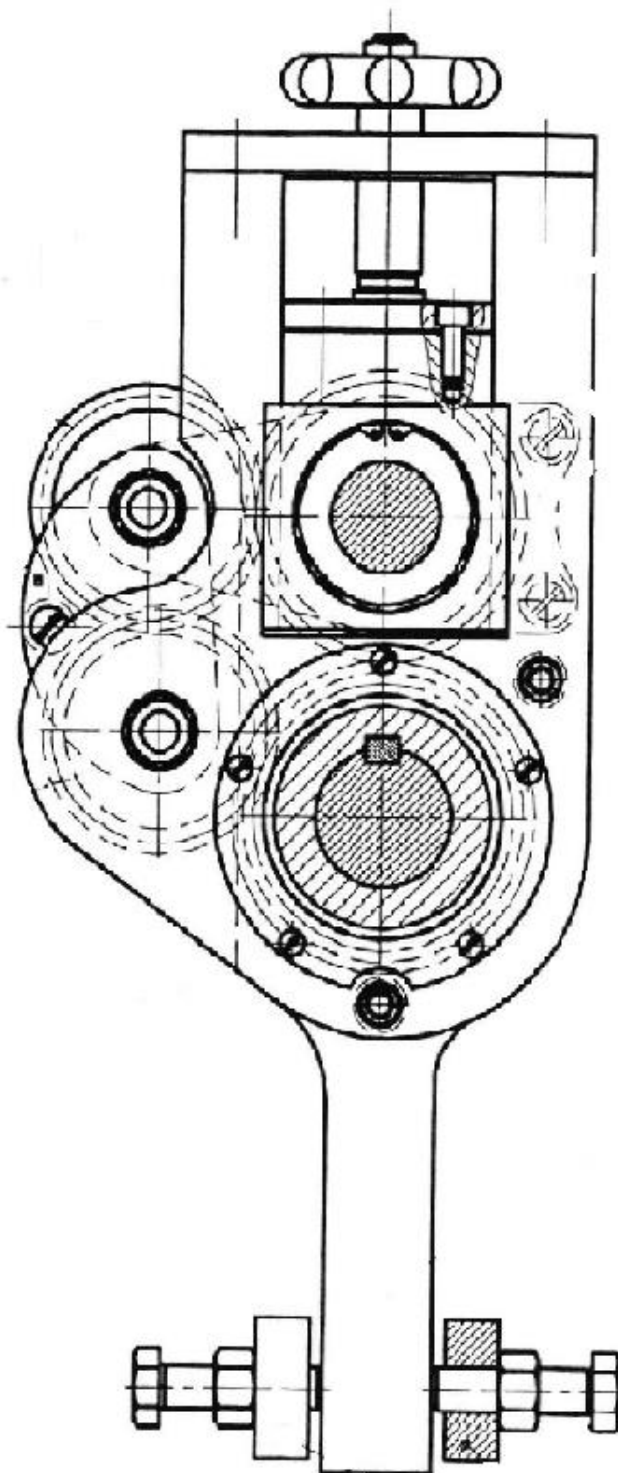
Шестеренная клетка с корпусом выполненным со станиной
